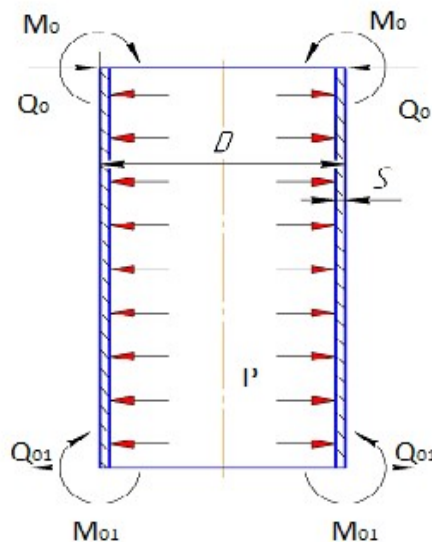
Розрахункова схема циліндричної обичайки
